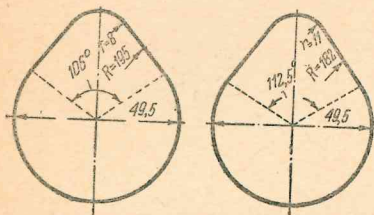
Профиль всасывающего и выпускного кулачков двигателя «Сталинец-60» ЧТЗ
